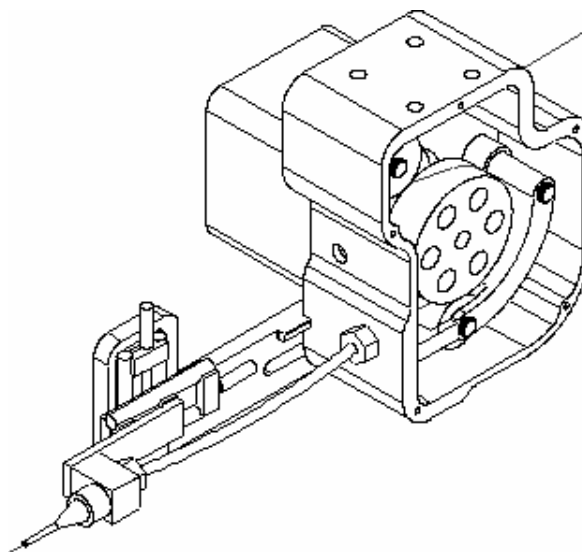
„Tlačný“ podavač drátu pro svářečku ⁽¹²⁾
